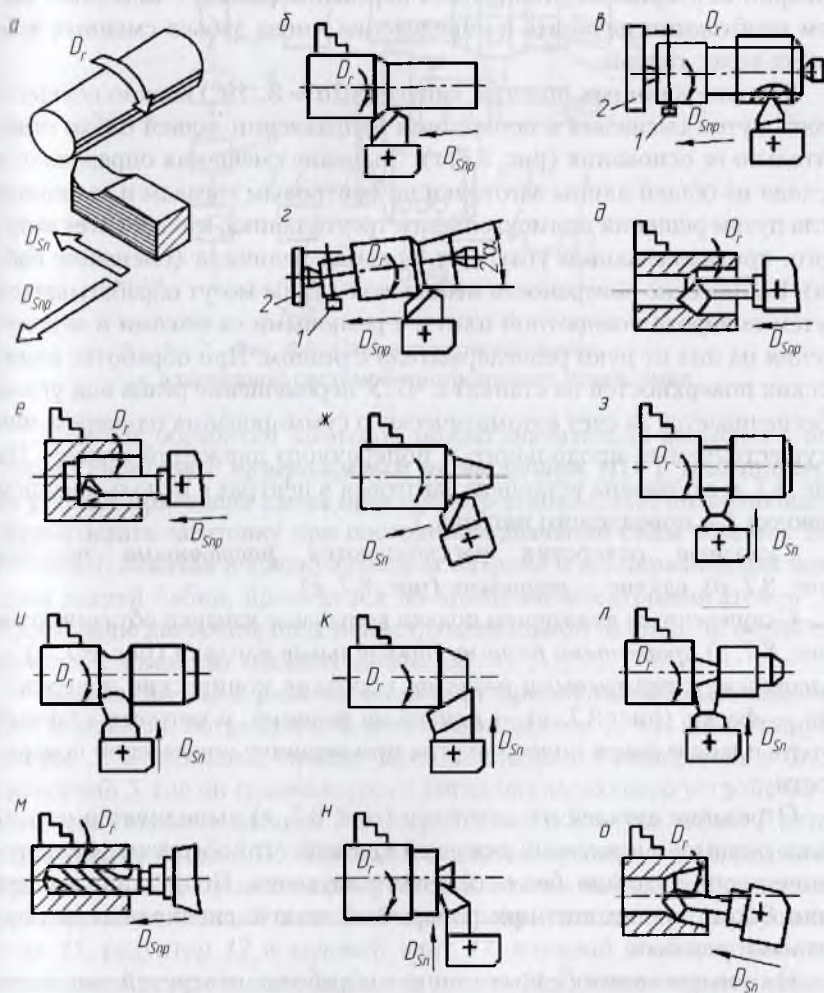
Схемы обработки заготовок на токарных станках:
